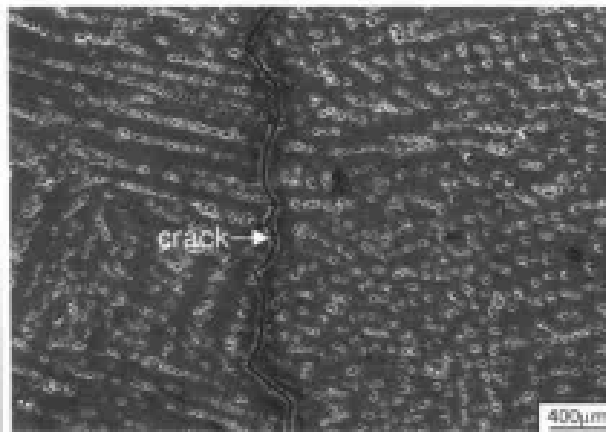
激光焊接, 42CrMo 合金/42CrMo 合金, CO<sub>2</sub> 激光, 焊缝, 功率 3200W, 焊接速度 2m/min
